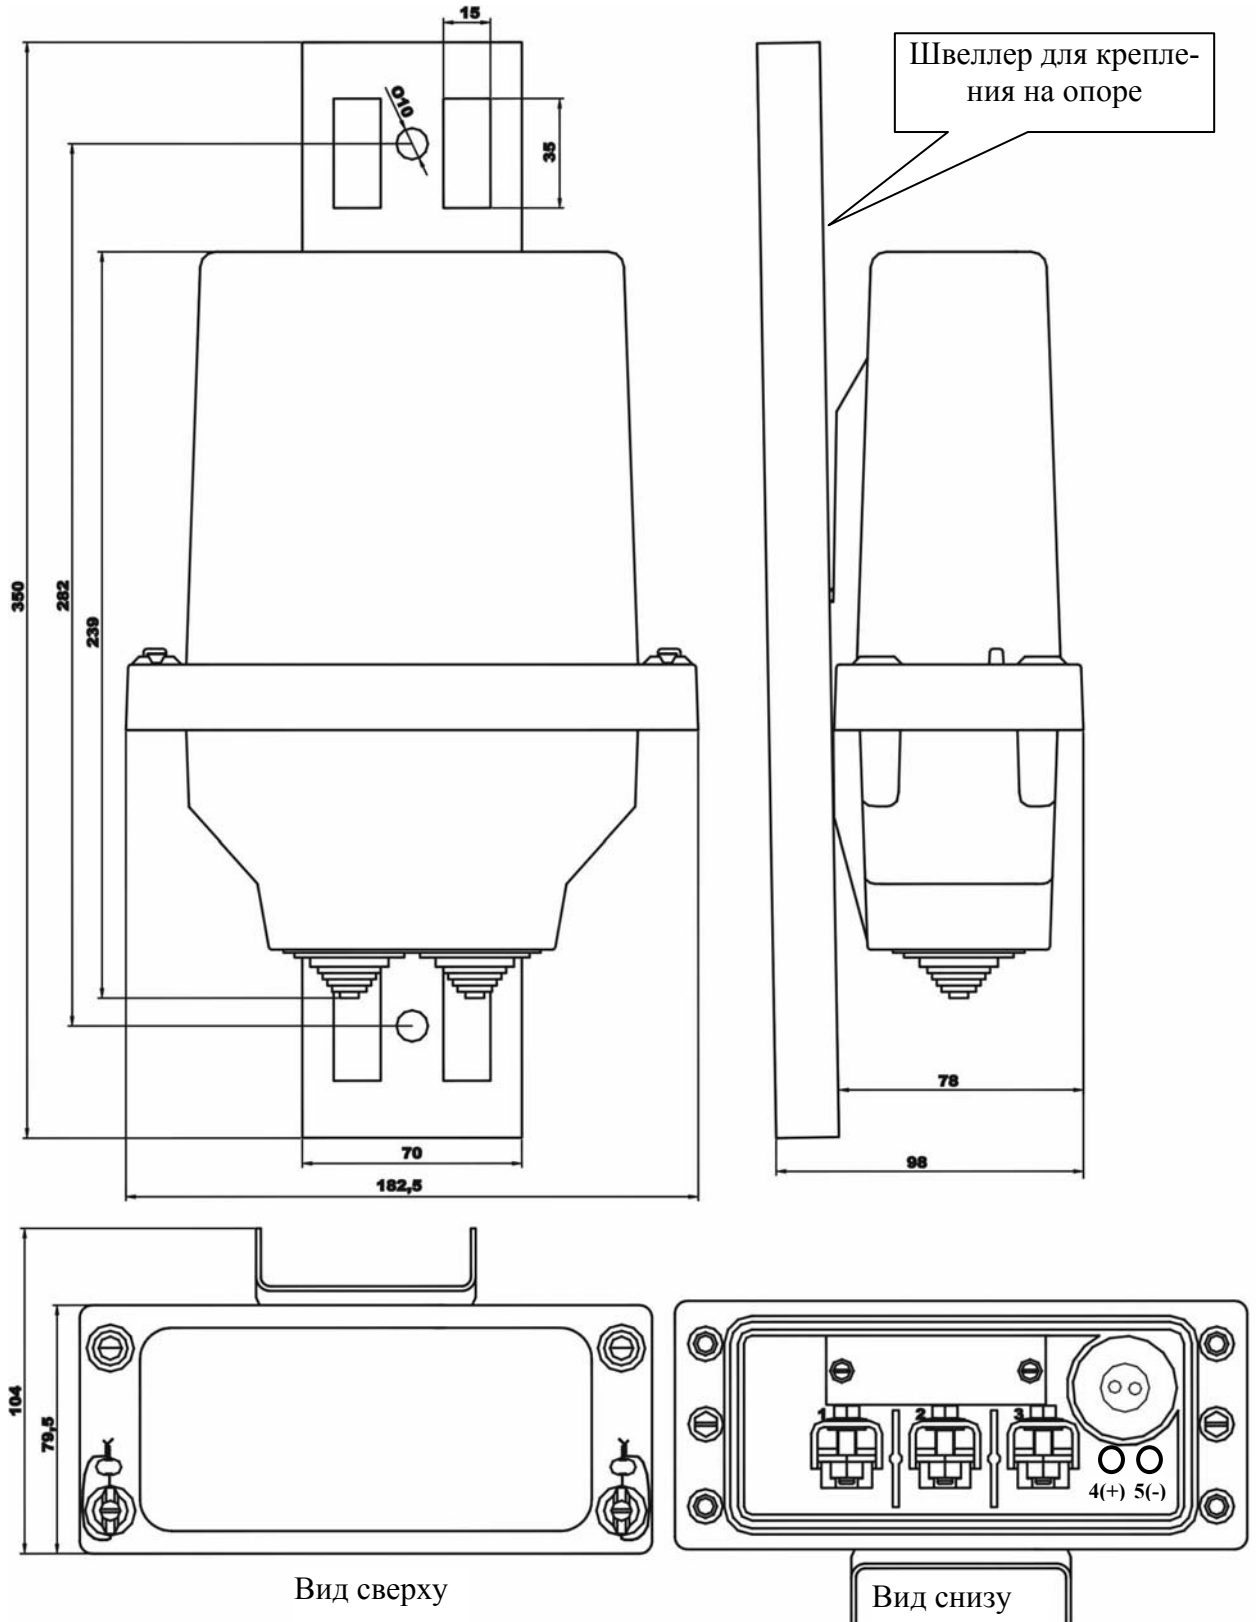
Габаритный чертеж и установочные размеры счётчиков
